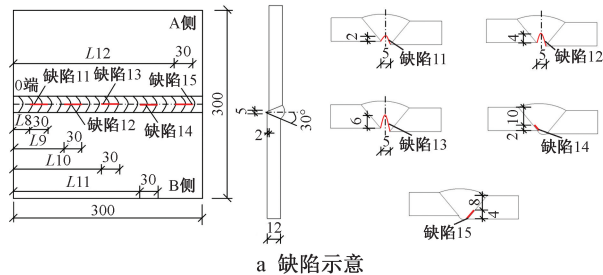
试件 JMHS-221227 焊缝缺陷设置
